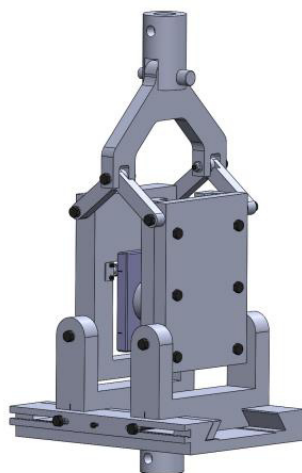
Schéma přípravku sada 2 pro minimální a maximální délku vzorku
